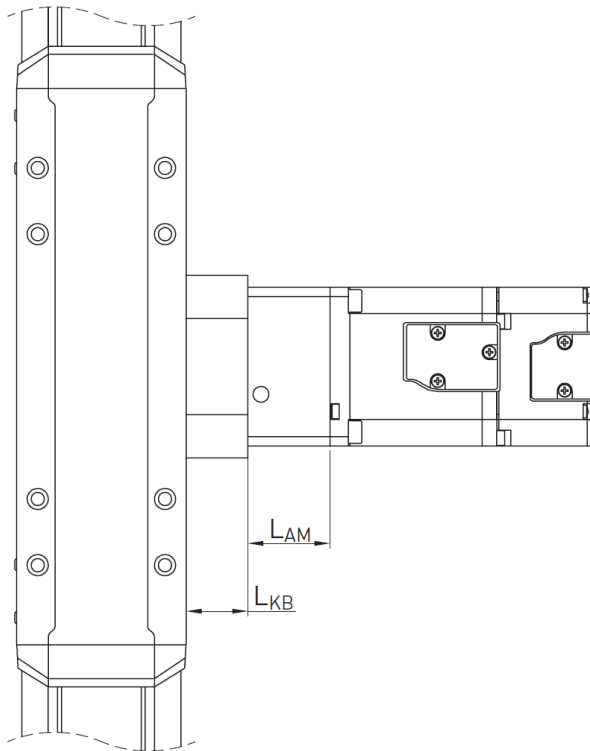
Motoranbindung Brückennachse HB-B ohne Getriebe
